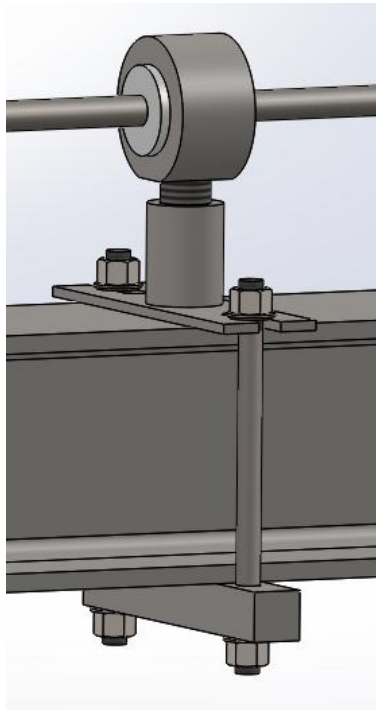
Suporte de Barras montado na Viga (modelado no SolidWorks 2015)
